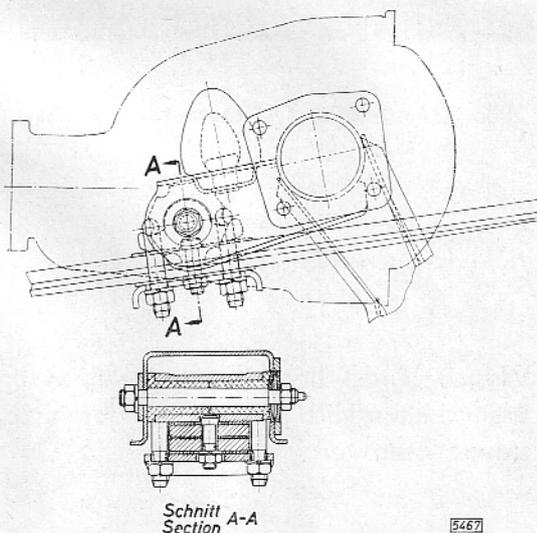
Befestigung Hinterachse an Hinterfeder
